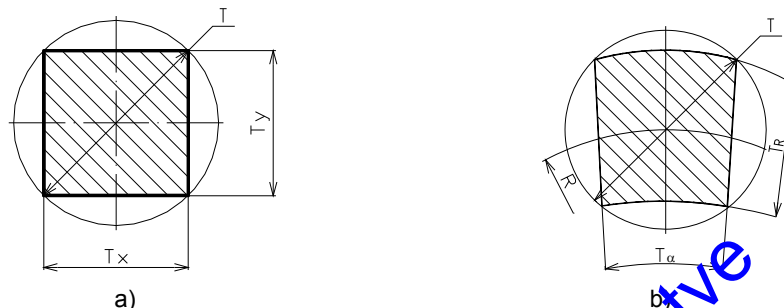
Predpis tolerance menovitej polohy osí dier na rozstupovej kružnici
